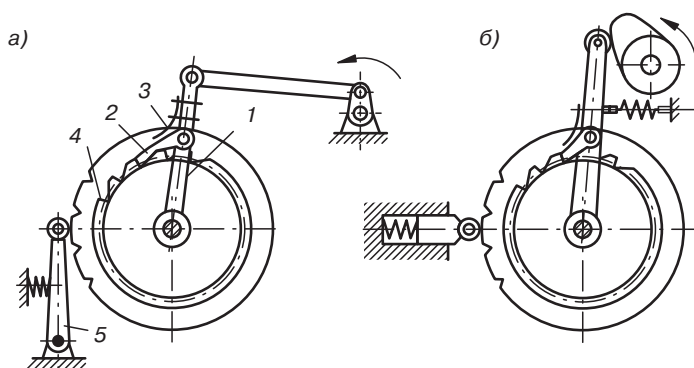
Схемы храповых механизмов: а — с рычажным приводом; б — с кулачковым приводом; 1 — коромысло; 2 — собачка; 3 — пружина; 4 — храповое колесо; 5 — фиксатор
